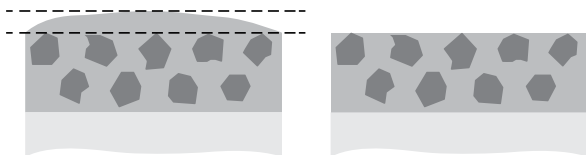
Ziel des Abrichtens: Erzeugen der Makrogeometrie
